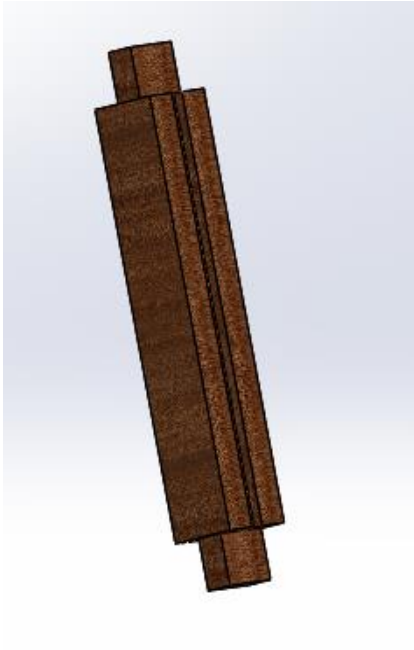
Mástil, pieza central de la parte baja del carro, e.p.
